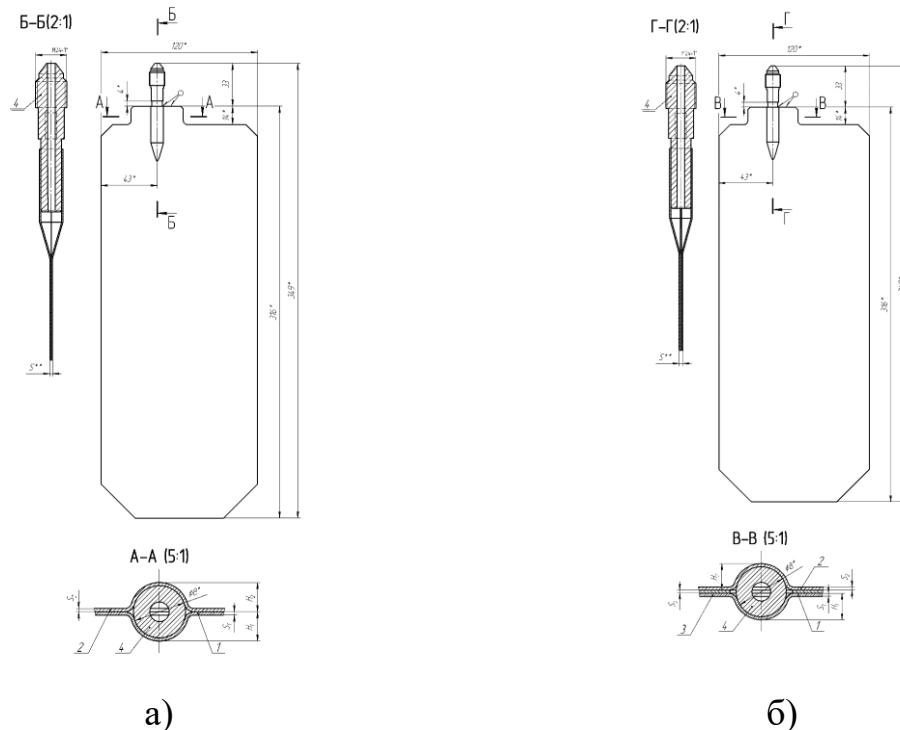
Заготовка елемента порожнистої лопатки: а) збірна заготовка з 2-х титанових листів та штуцера; б) збірна заготовка з 2-х титанових листів та штуцера
